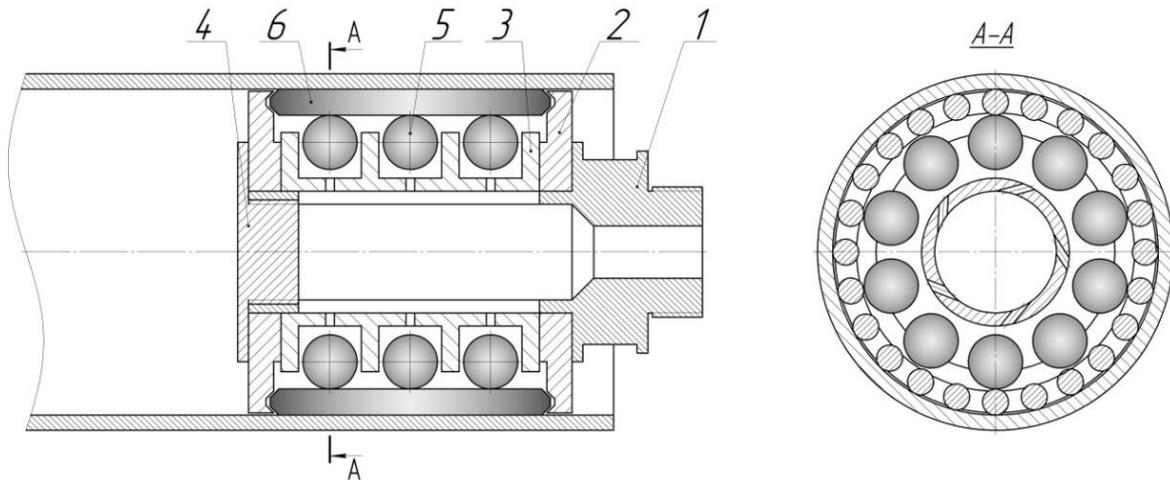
Комбинированный импульсно-ударный центробежный раскатник.
